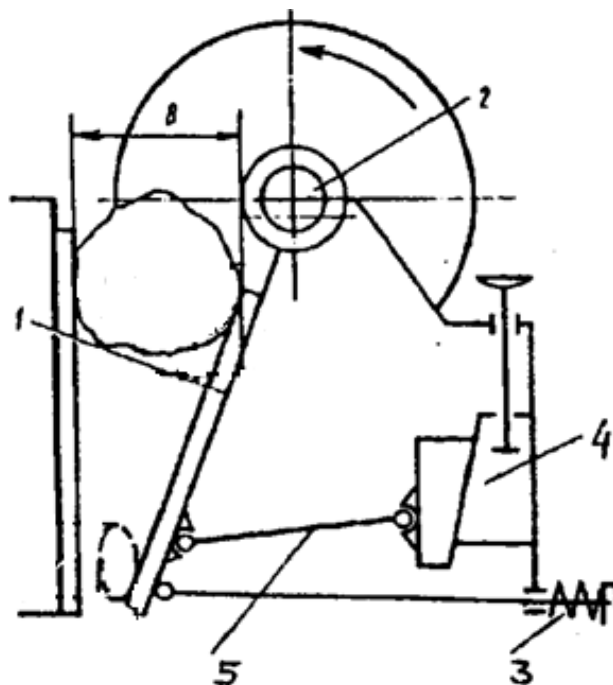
Кінематична схема щокової дробарки із складним хитанням рухомої щоки [3]
